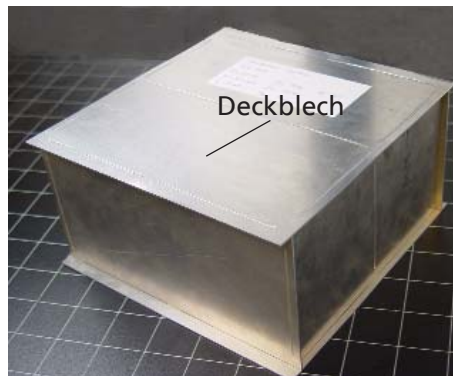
Laserstrahlgeschweißter Demonstrator
